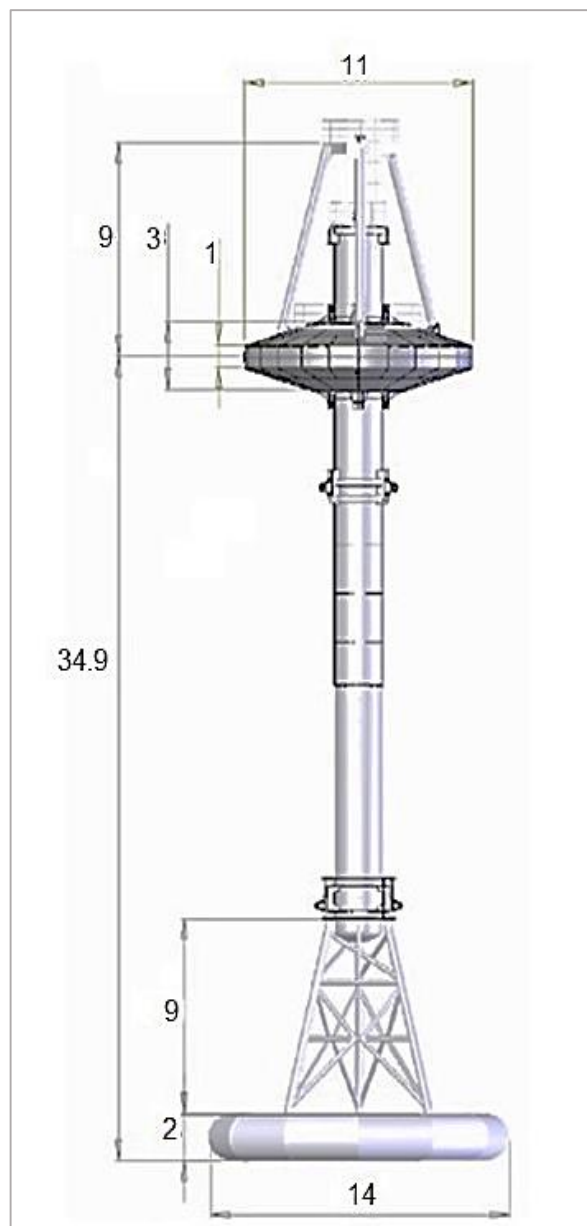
5: Dimensiones del dispositivo Power Buoy en metros
